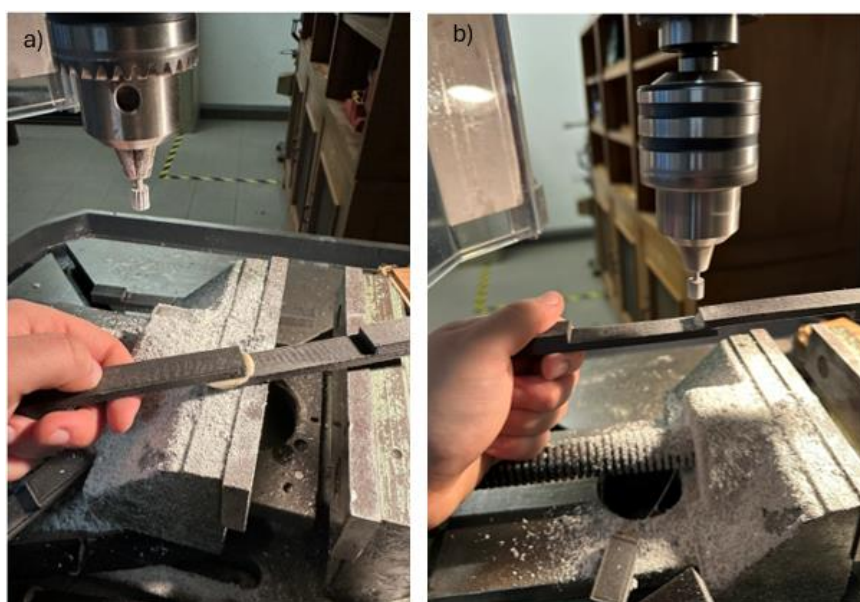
Remoção de excessos; a) antes de remover excessos; b) depois de remover excessos
